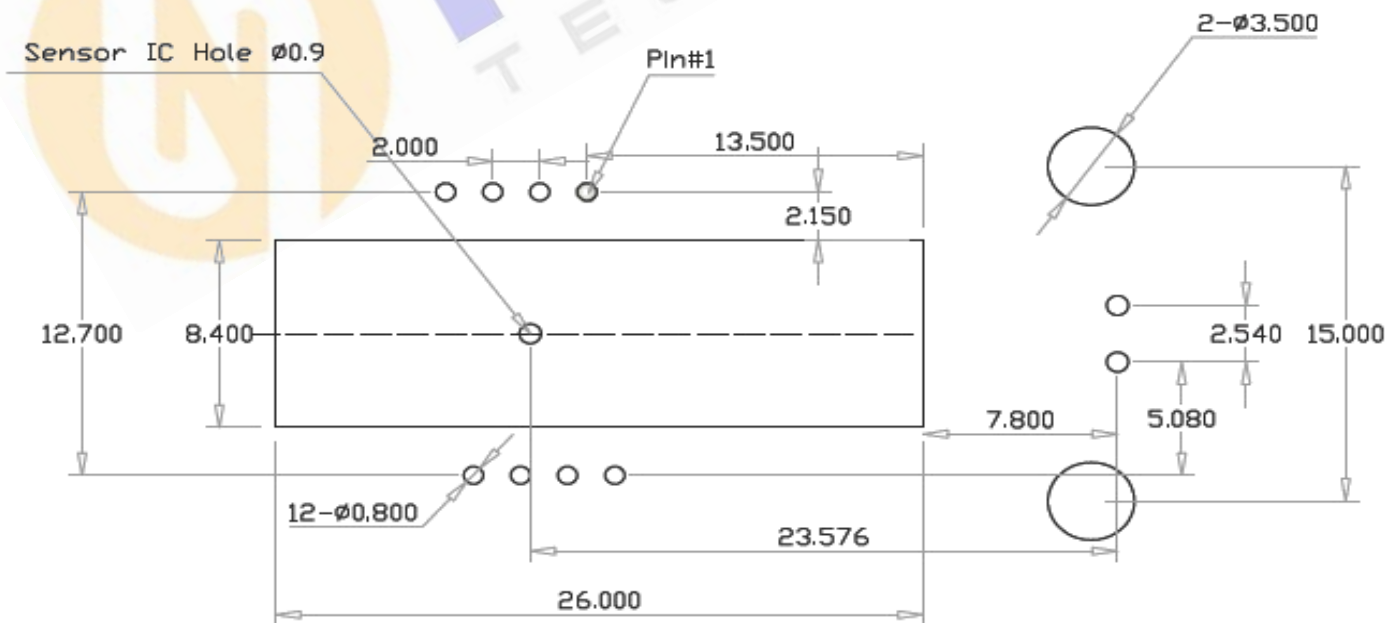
推荐 PCB 机械尺寸 (mm/inch)
